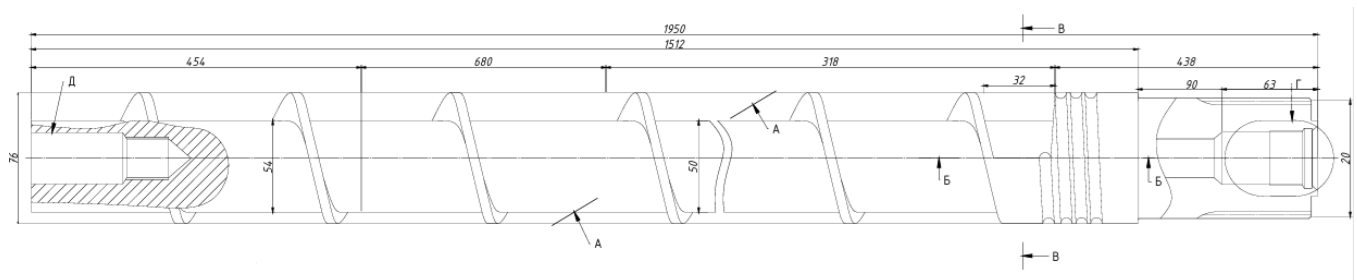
Конструкція черв'яка екструдера з основними розмірами
